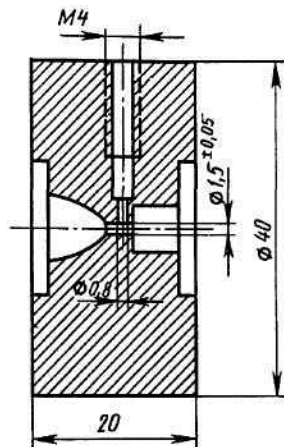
Робоча ділянка (сопло) установки ТД-4
